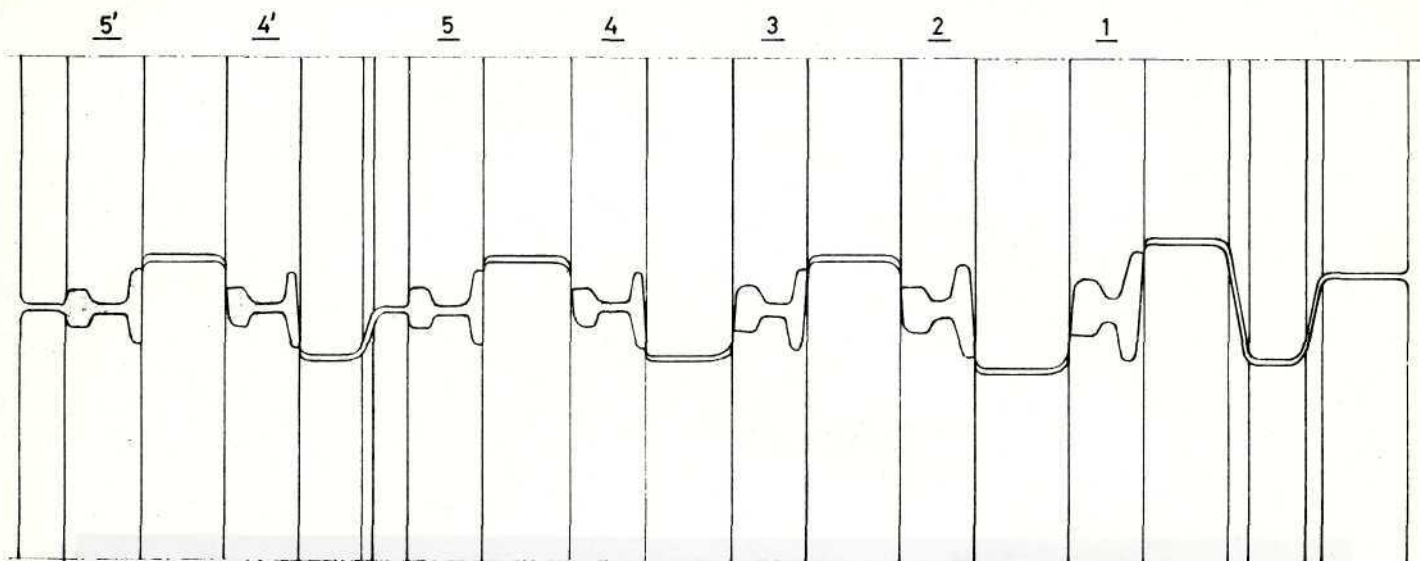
Eerste doorgang van de voorbereider: plat walsen van de bloom.
